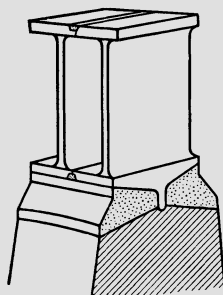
Auf Scheibe aufgeschweißte Laufschaufeln
